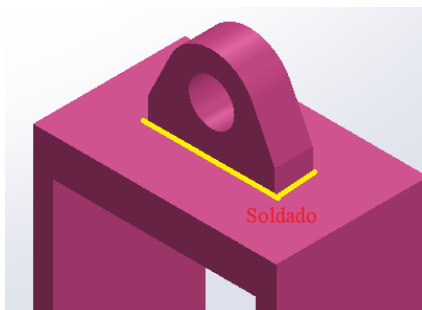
Vista detalle de soldado de pieza N°13 parte superior (Fuente 102)
